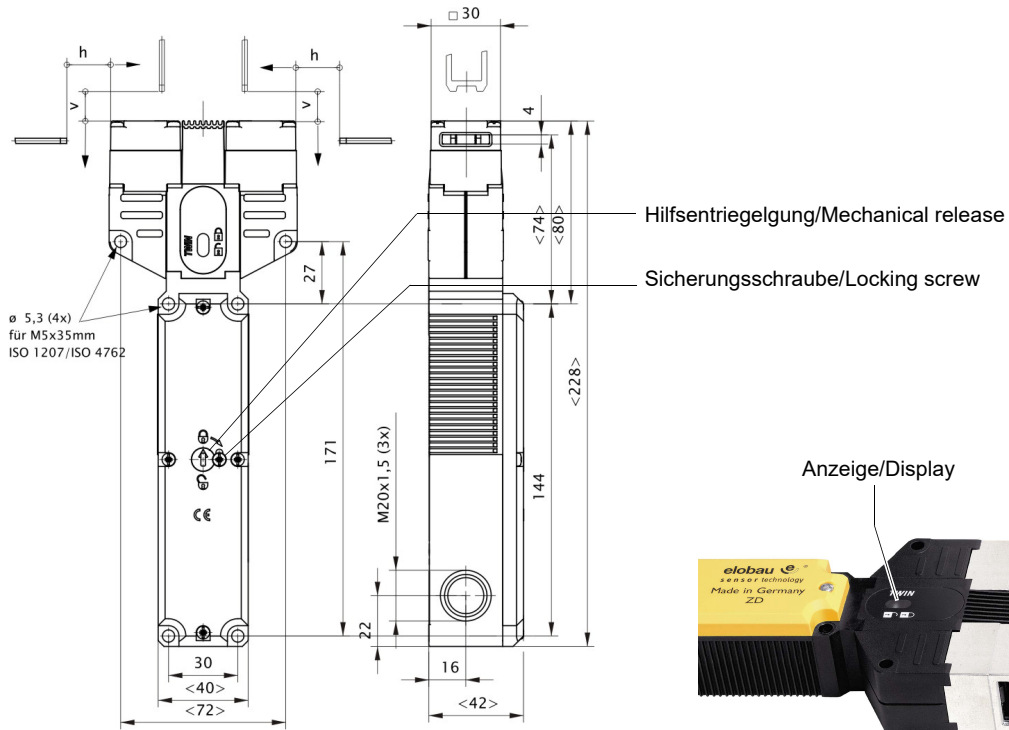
Maßzeichnung ZD/Dimensional drawing ZD
